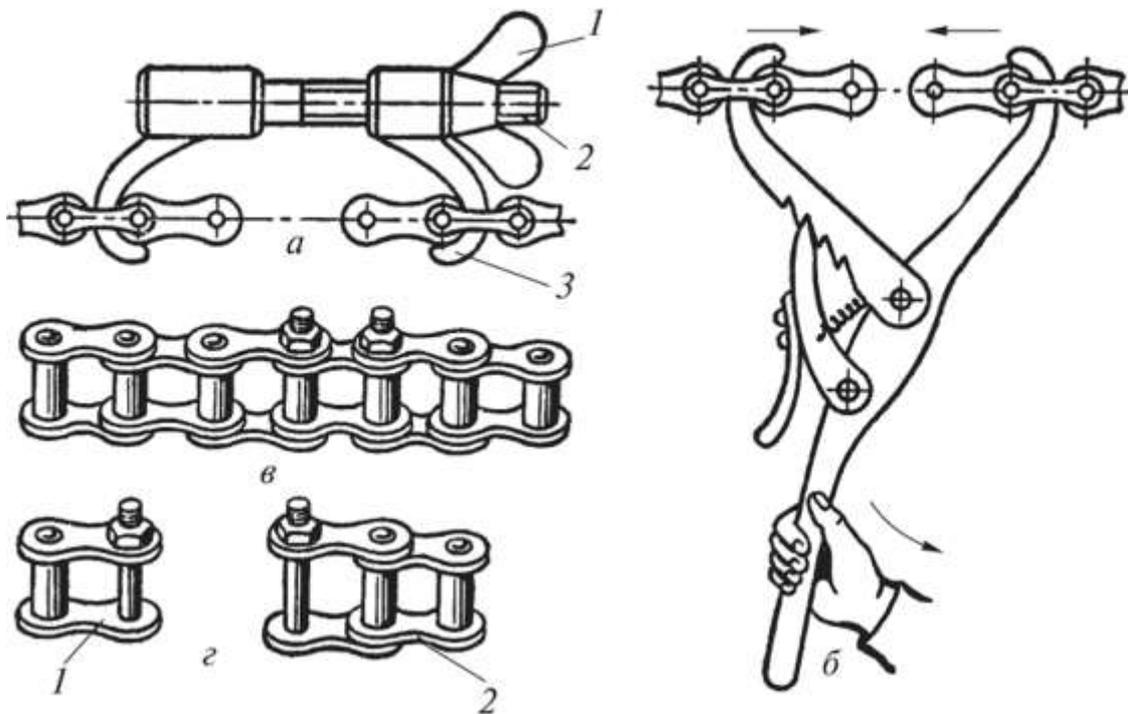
Приспособления для натяжения и соединения цепей при сборке: *a* — винтовыми стяжками: 1,3 — лапки; 2 — винт с правой и левой резьбой; *б* — пружинными стяжками; *в* — отрезок цепи, собранной из соединительных звеньев; *г* — соединительные звенья: 1 — переходное; 2 — обыкновенное
